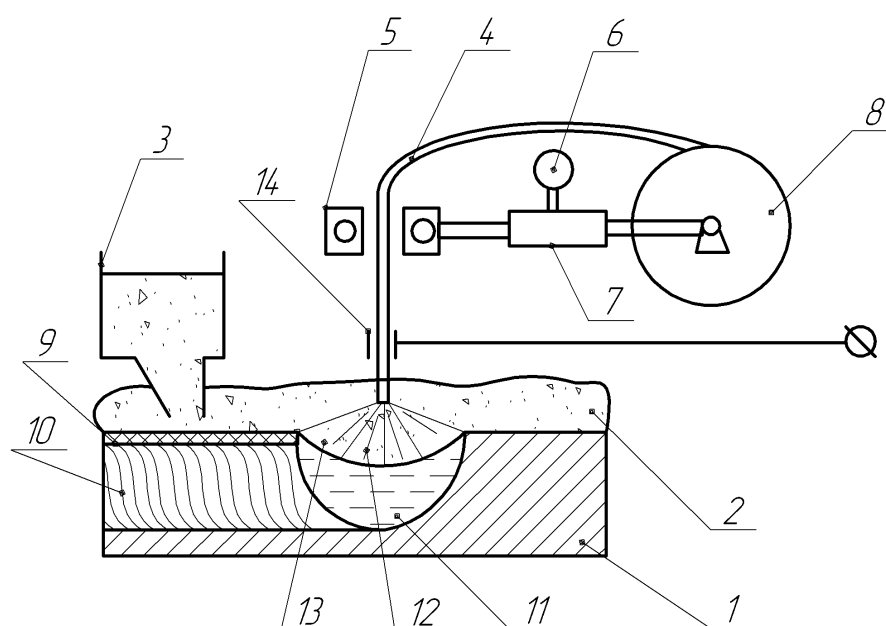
Схема автоматизированной дуговой сварки под флюсом
